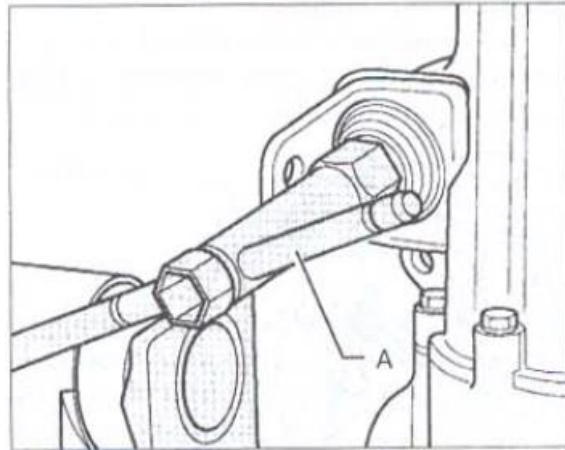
Схема зняття кришки вала керування перемиканням передач
